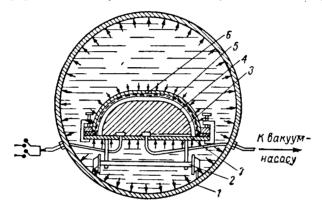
Схема автоклавного способа формования: 1 — автоклав; 2 — тележка; 3 — болванка прессформы; 4 — пакет стеклоткани, пропитанной связующим; 5 — цулага с электрообогревом; 6 — резиновый чехол; 7 — плита основания.
